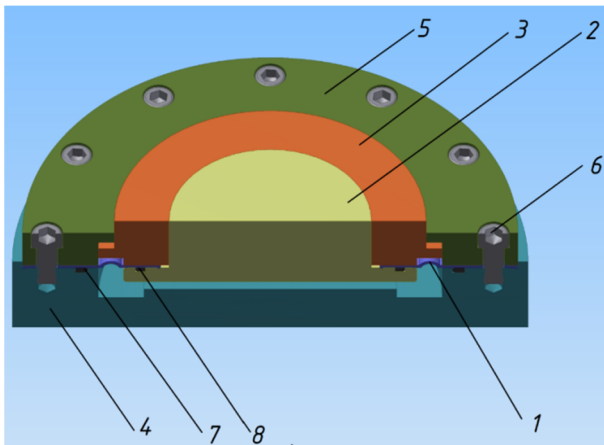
Конструкція ГММ в розрізі: 1 – мембрана; 2 – пунжер; 3 – втулка; 4 – корпус; 5 – кришка; 6 – болти; 7, 8 – ущільнення
